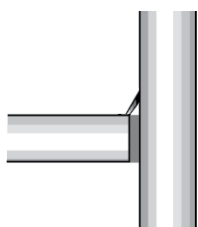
Brecha de 2,5 mm (3/32 pulgadas) después de soldadura
